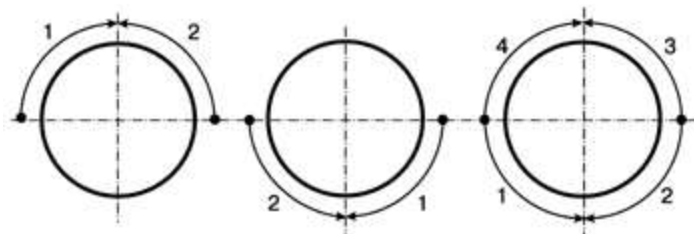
Сварка в поворотном стыке труб корневого шва в два поворота двумя сварщиками:
